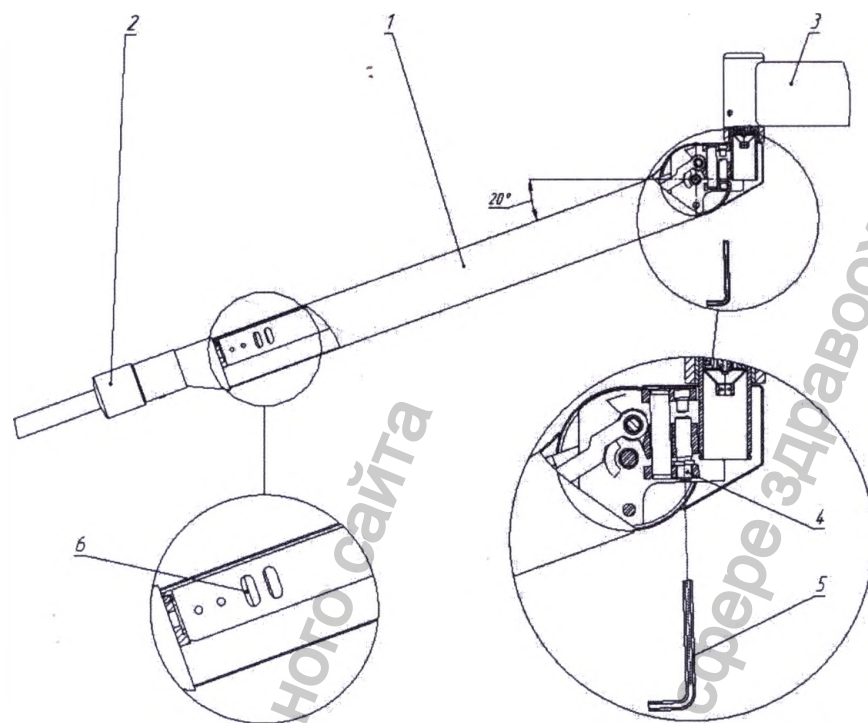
Регулировка угла подъема консоли пружинной
